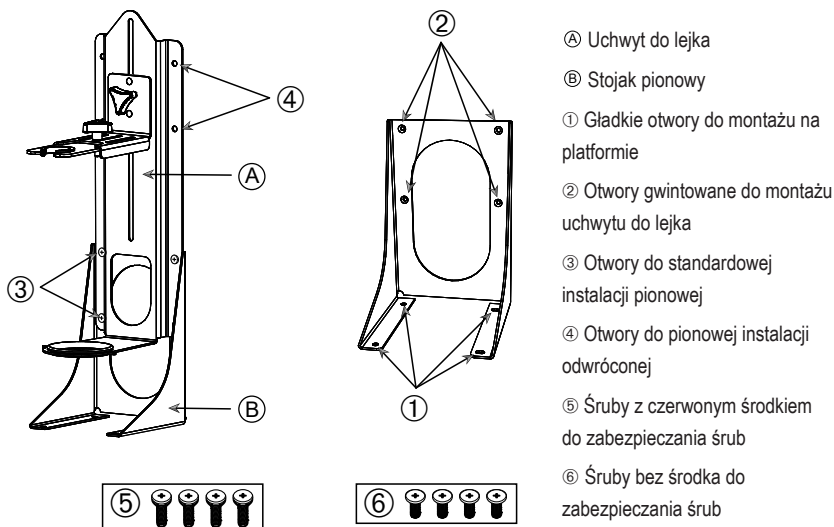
Pozycje montażowe uchwytu do rozdzielacza
